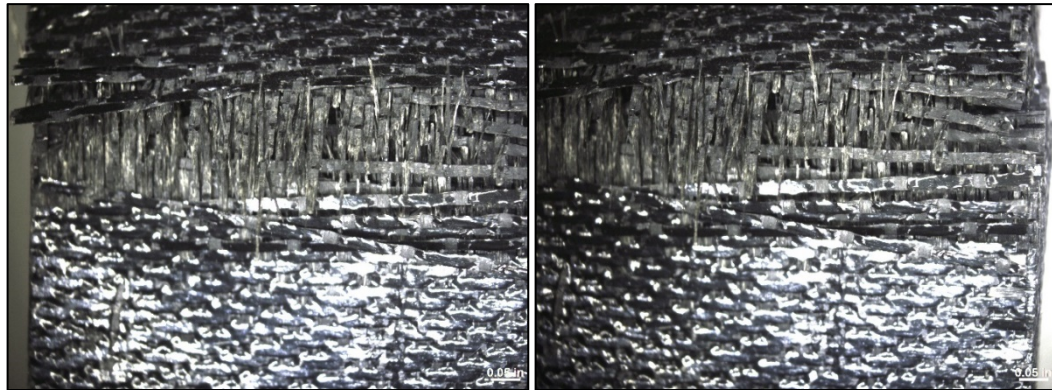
Inspección visual de probeta 10 de 12 capas a 6000 lbf, que presenta un código de falla AGM a) extremo izquierdo y b) extremo derecho de la probeta con fractura expuesta.
